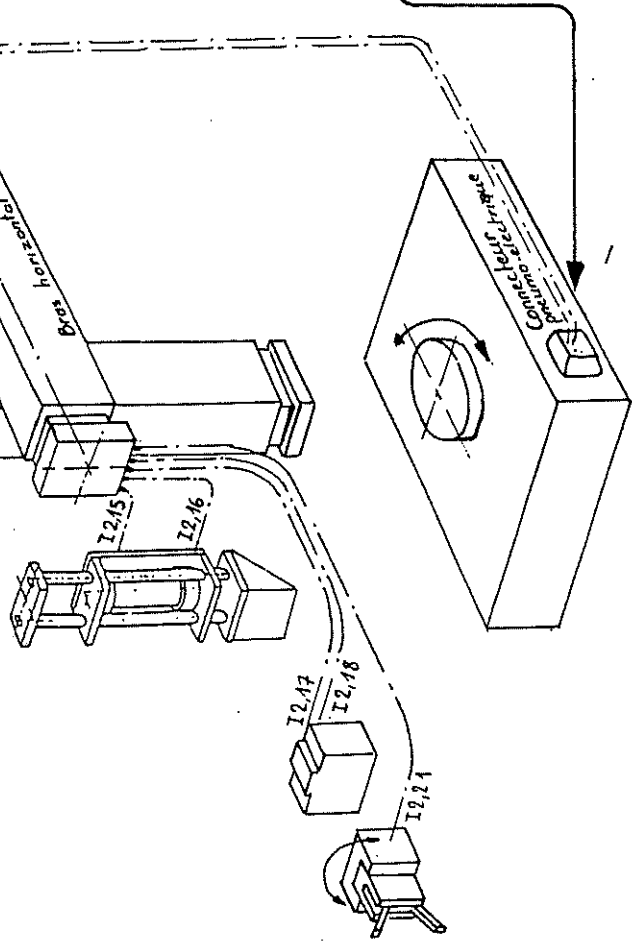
DETAIL. RACCORDEMENT BRAS HORIZONTAL
